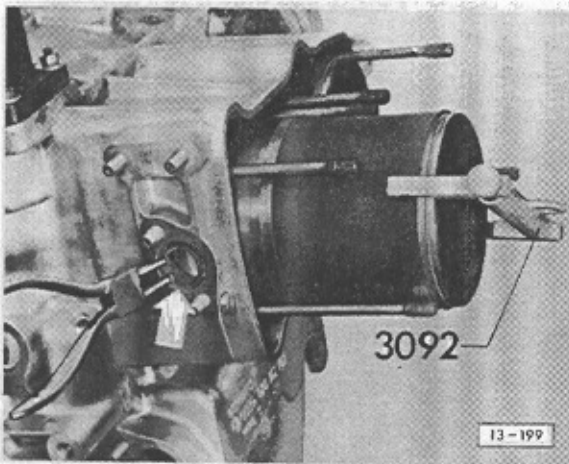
Kolben und Zylinder kennzeichnen
